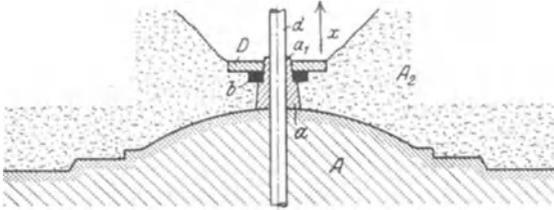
Aufgestampfter Oberkasten zu Fig. 111.
